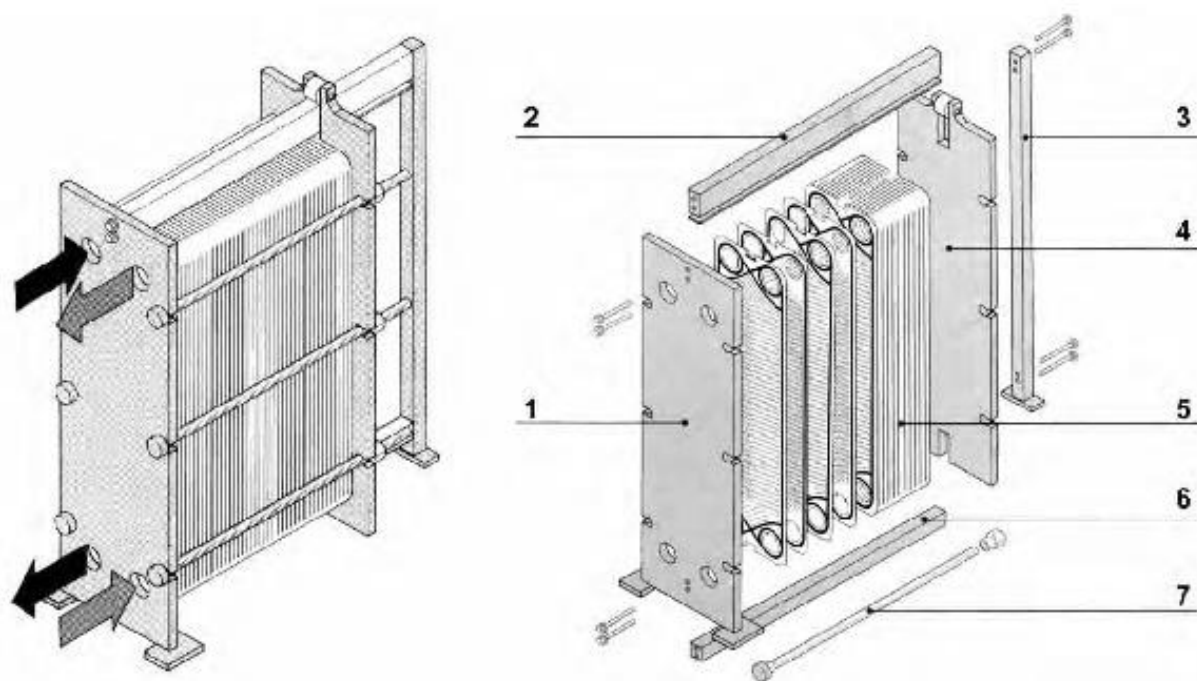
Схема рассчитываемого теплообменника в разборе: 1 - плита неподвижная; 2 - направляющая верхняя; 3 - стойка задняя; 4 - плита прижимная; 5 - пакет пластин с прокладками; 6 - направляющая нижняя; 7 - шпильки стяжные.
